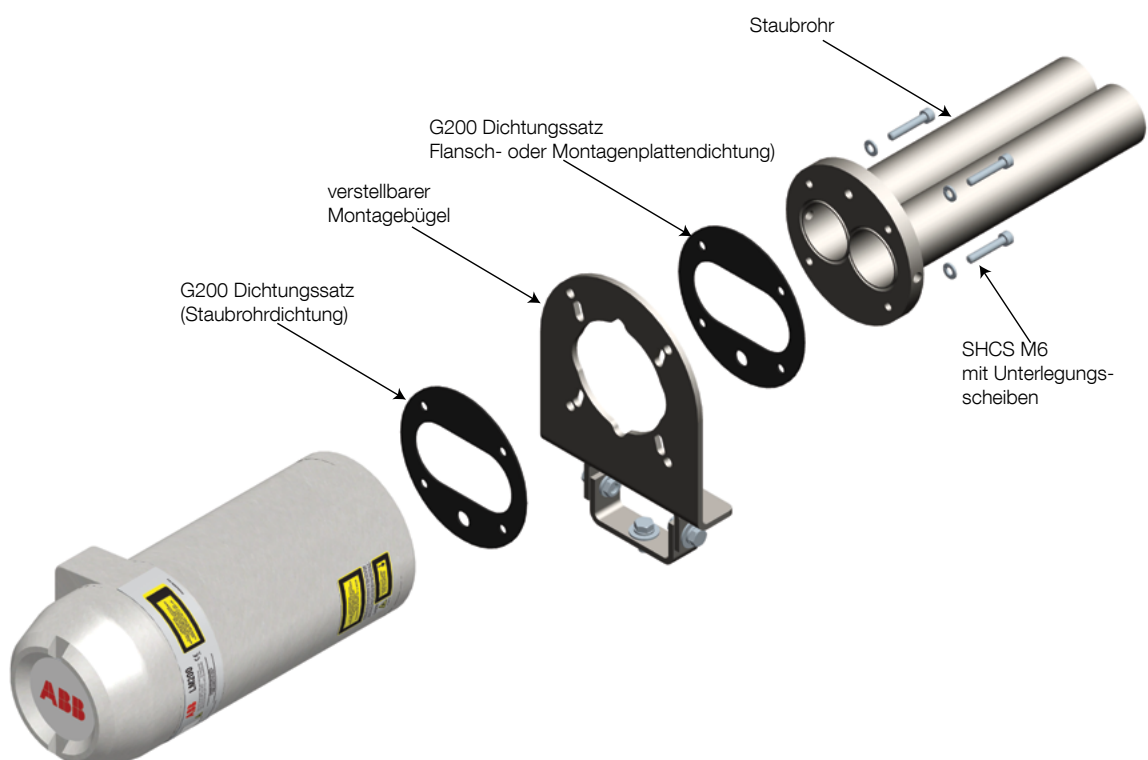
15. Staubrohr mit einstellbarer Montagehalterung
